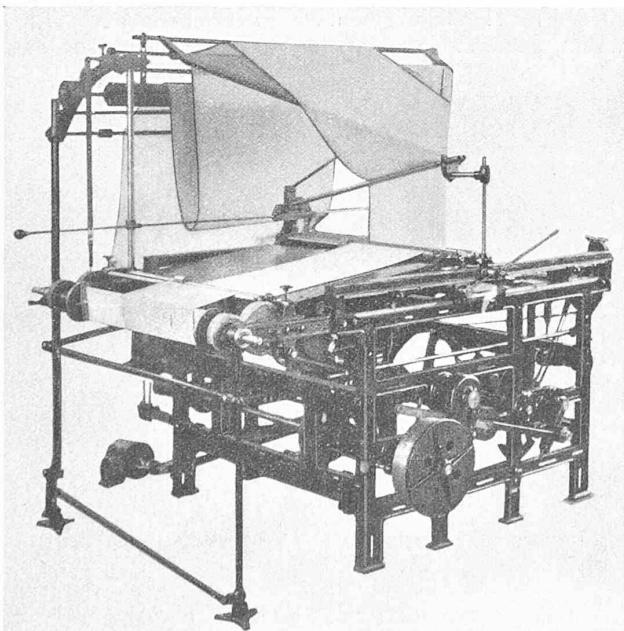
Doublier-, Mess- und Legemaschine, kombiniert mit Wickelvorrichtung.
